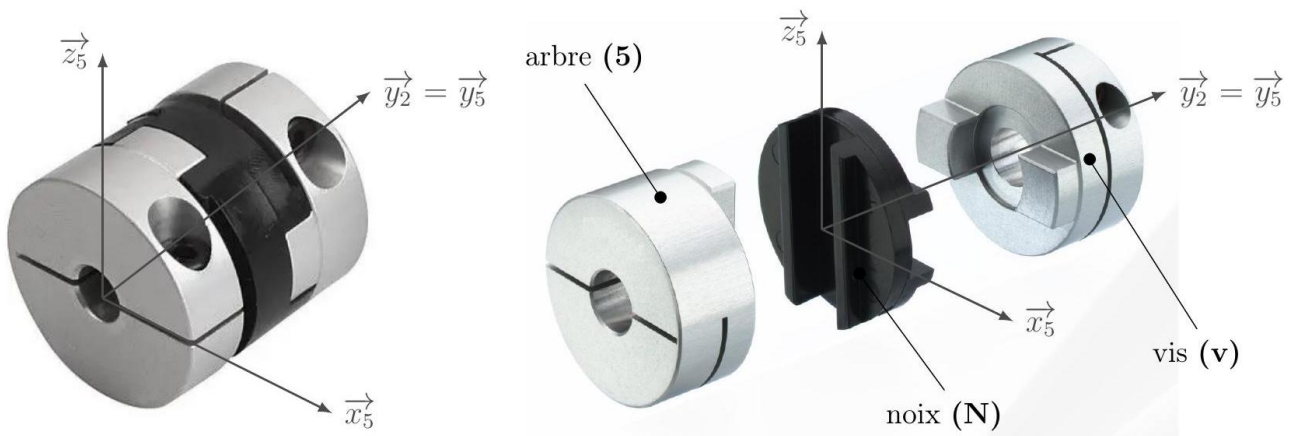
Joint d'Oldham assemblé (à gauche) et éclaté (à droite)
